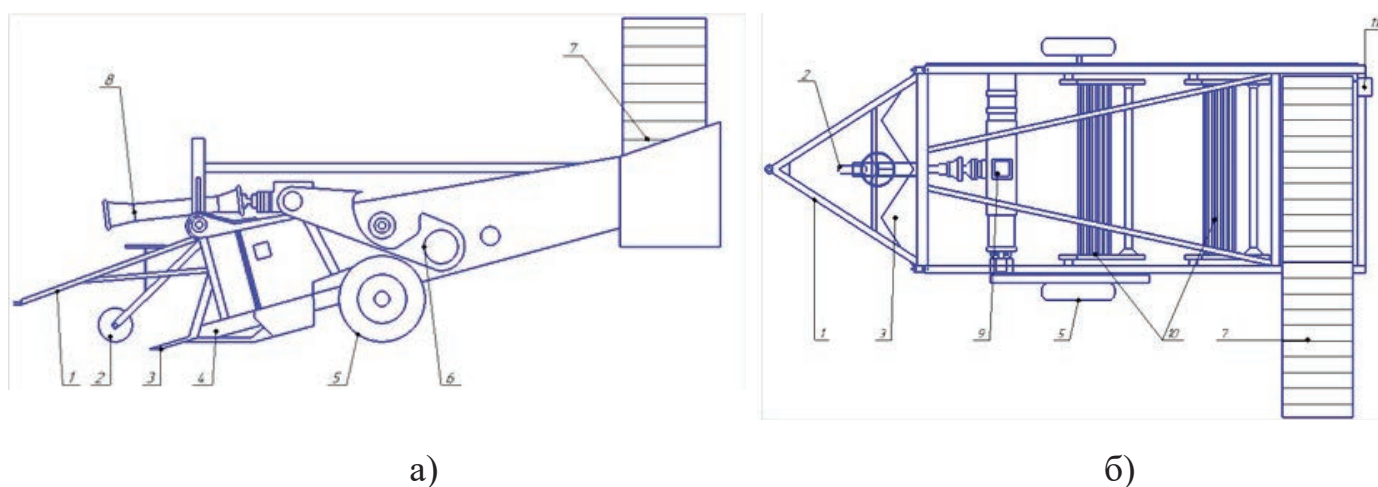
Схема машины для уборки корнеклубнеплодов (а – вид сбоку; б – вид сверху):
